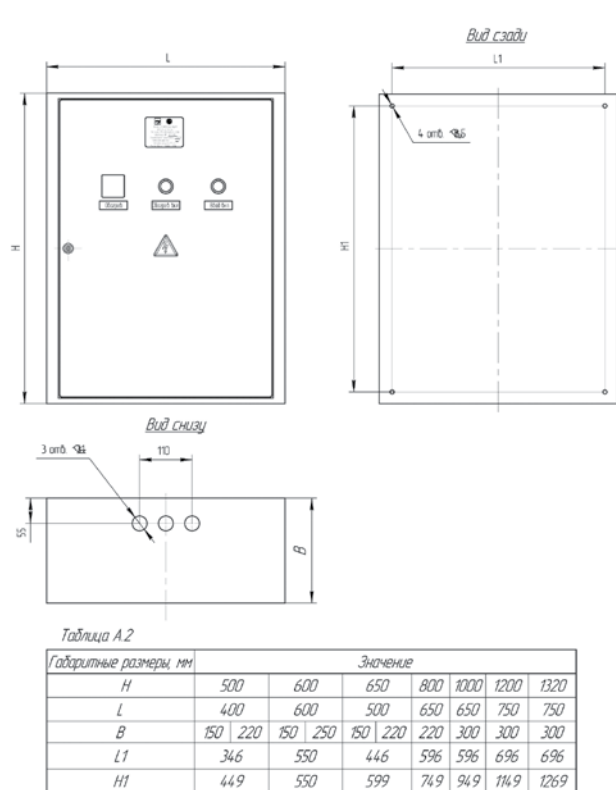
Общий вид и габаритные размеры шкафов ШСН навесного исполнения
